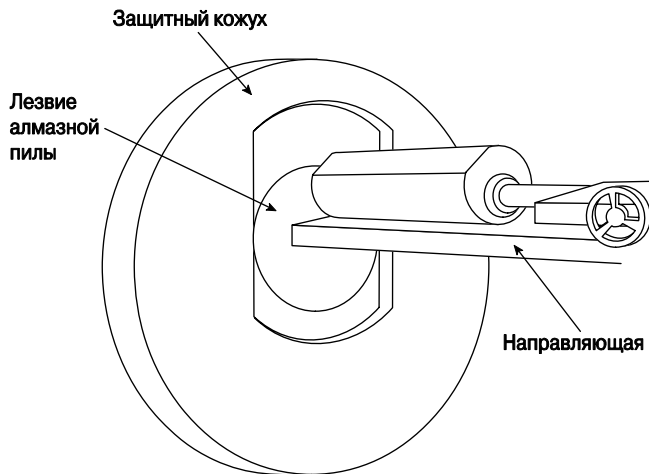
При изготовлении процессора заготовка разрезается алмазной пилой более чем на тысячу круговых подложек
